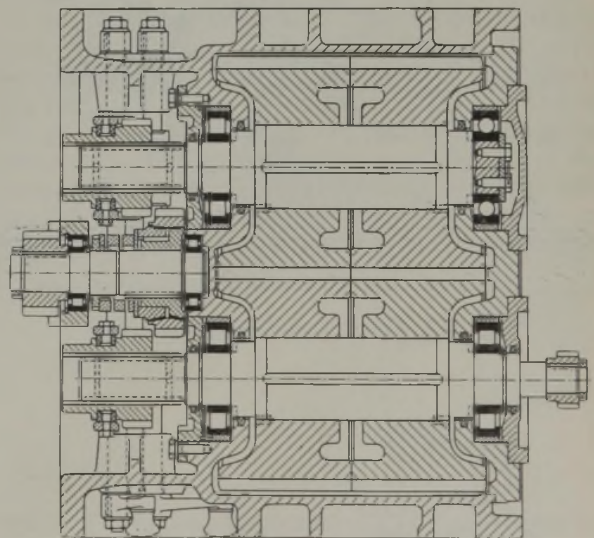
Pfeilradmotor einer Großschrämmaschine.
